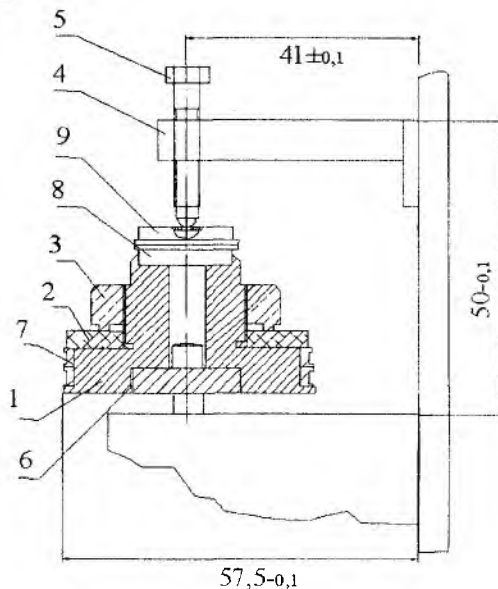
Конструкция устройства для лазерной сварки кольцевых швов корпусов ДА на установке «Квант-15»
